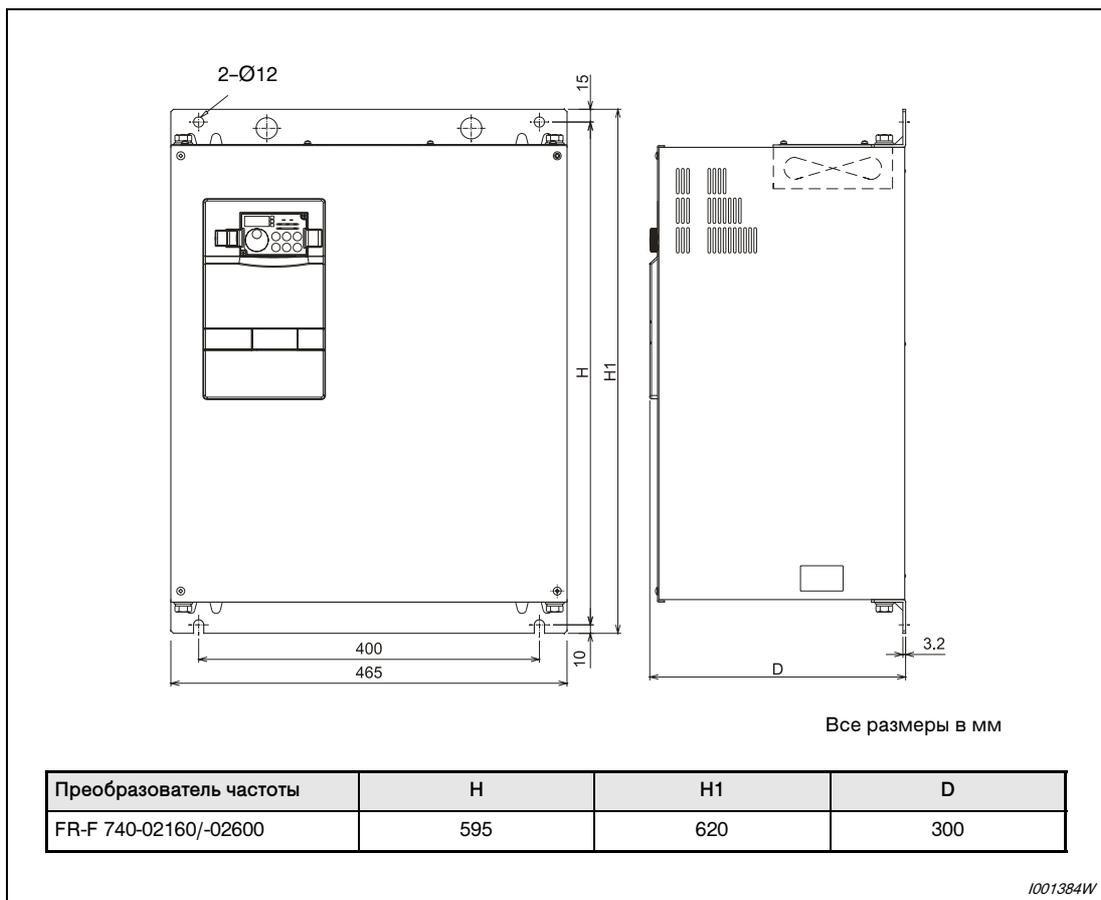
Размеры FR-A 740-02160 и FR-A 740-02600
